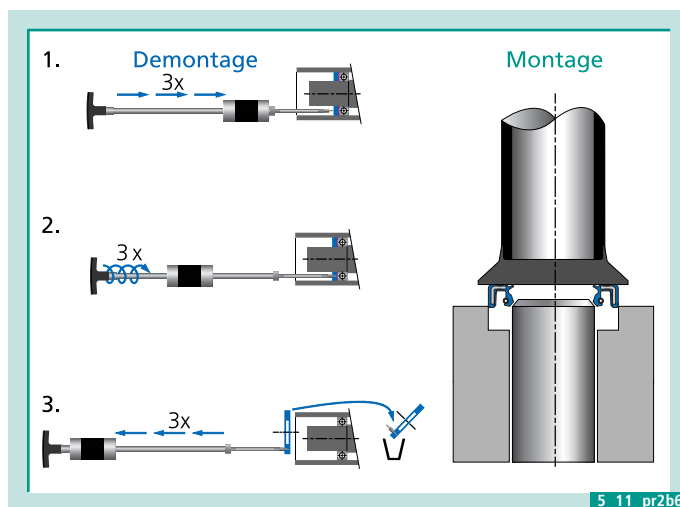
Demontage und Montage der Simmerringe. (Bild Freudenberg)
